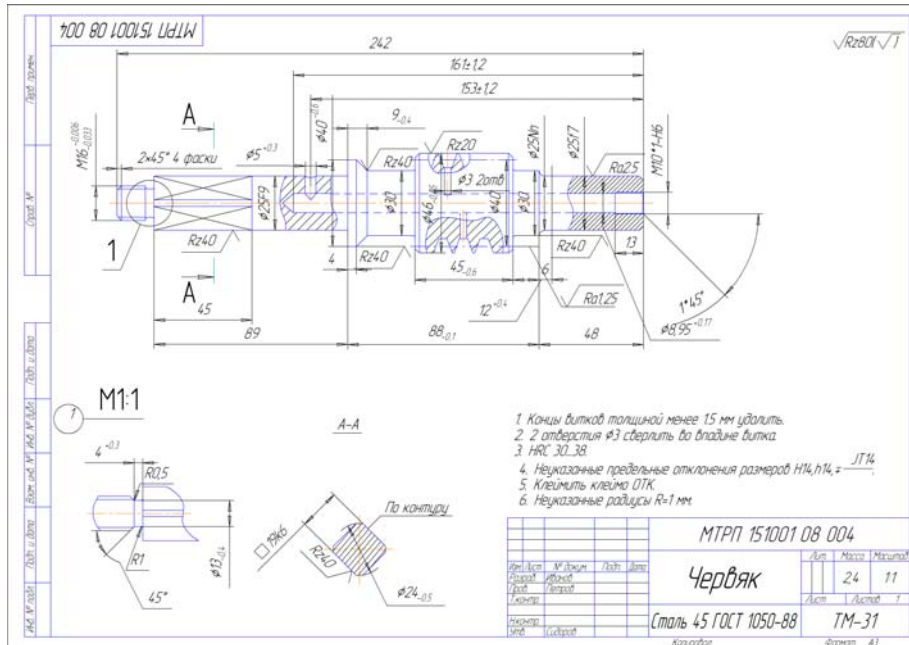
Чертеж детали, выполненный в САПР КОМПАС.
